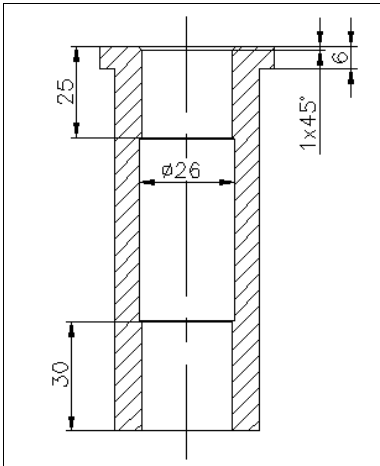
Чертеж втулки с нанесенными размерами без допусков
